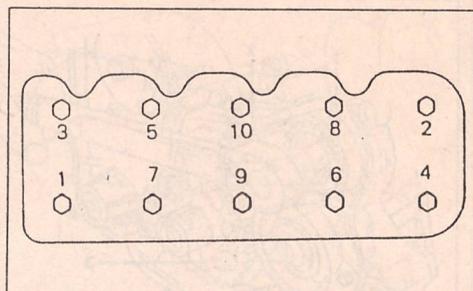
Последовательность отворачивания болтов крепления головки цилиндров (относится ко всем двигателям).
